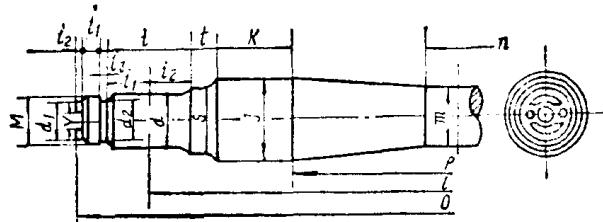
2 客、货车滚动轴承车轴各部分的尺寸
